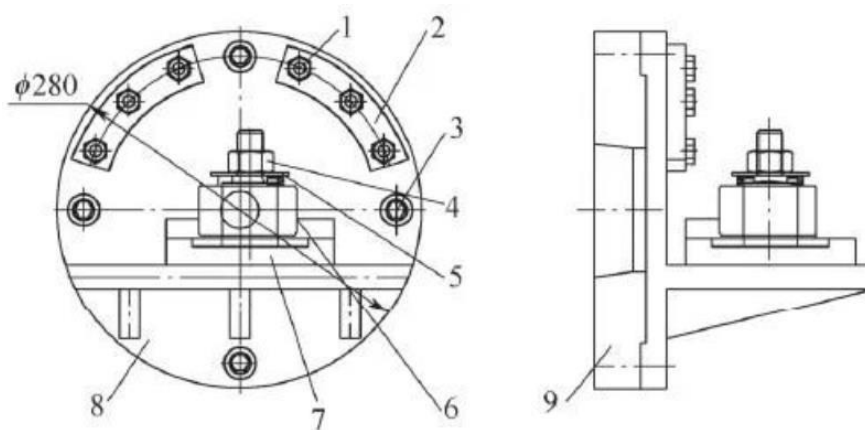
Разработка и сборка приспособления для обработки эксцентриковых отверстий в верхней торцевой крышке корпуса
